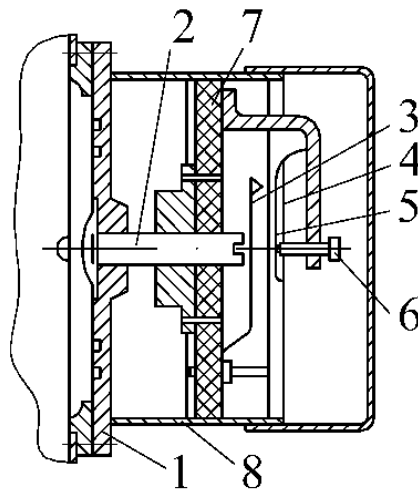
Вказівник рівня з металевою мембраною: 1 – мембрана; 2 – шток; 3 – контактний пристрій; 4 – кронштейн; 5 – пружина; 6 – гвинт регульовальний; 7 – плата; 8 – корпус
